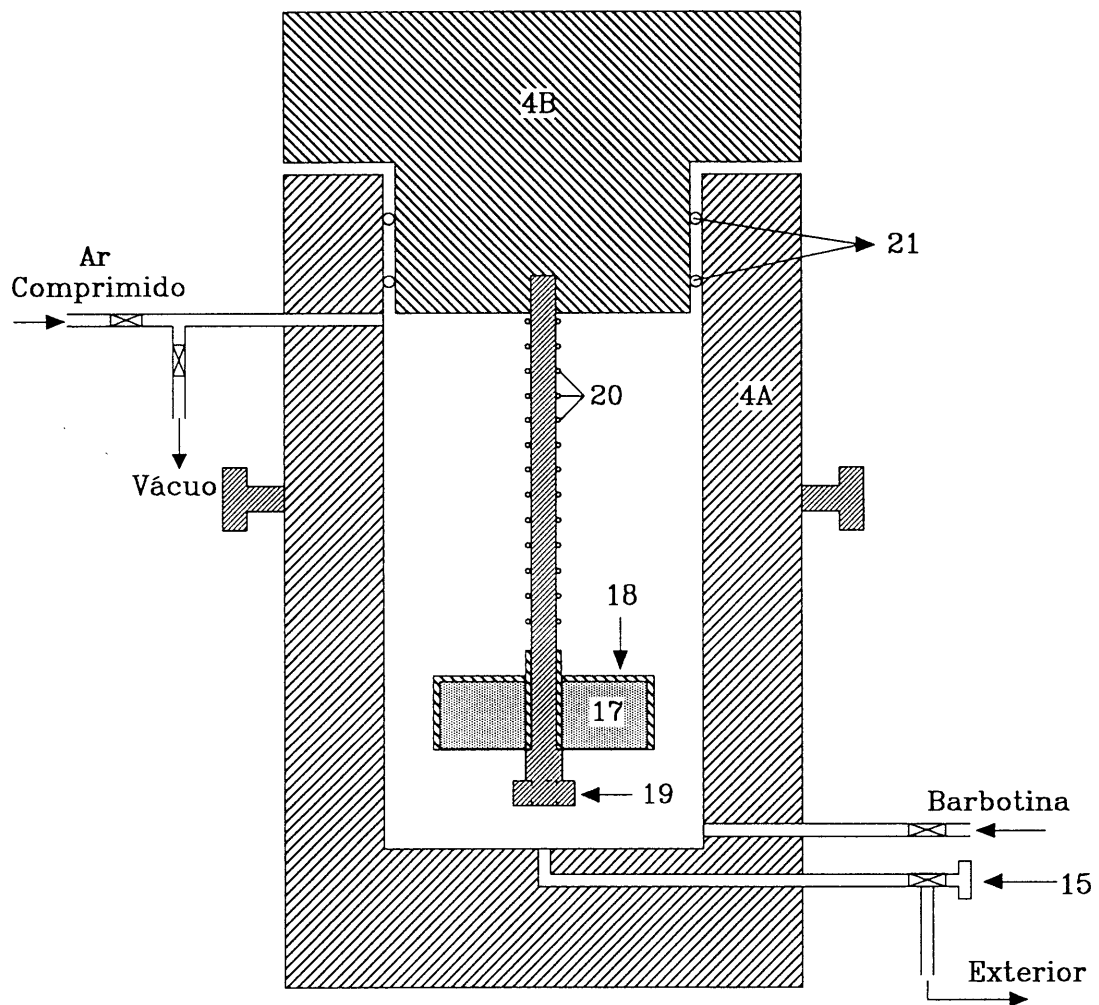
Desenho esquemático da panela de pressão e da montagem do molde: (4A), corpo da panela de pressão; (4B), tampa da panela de pressão; (17), molde de gesso; (18), cápsula metálica; (19), parafuso de suporte; (20), mola helicoidal; (21), anéis de borracha.
